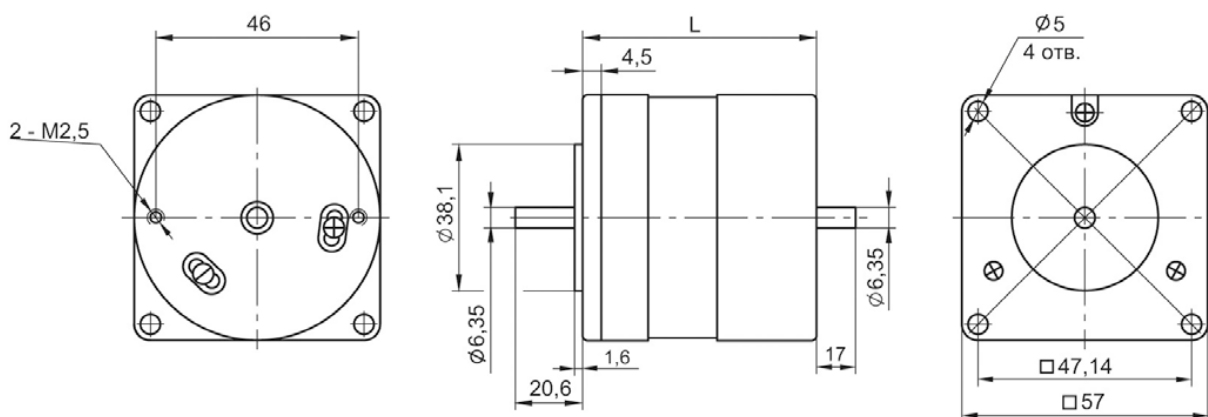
Габаритные и присоединительные размеры FL57BL(S)04
